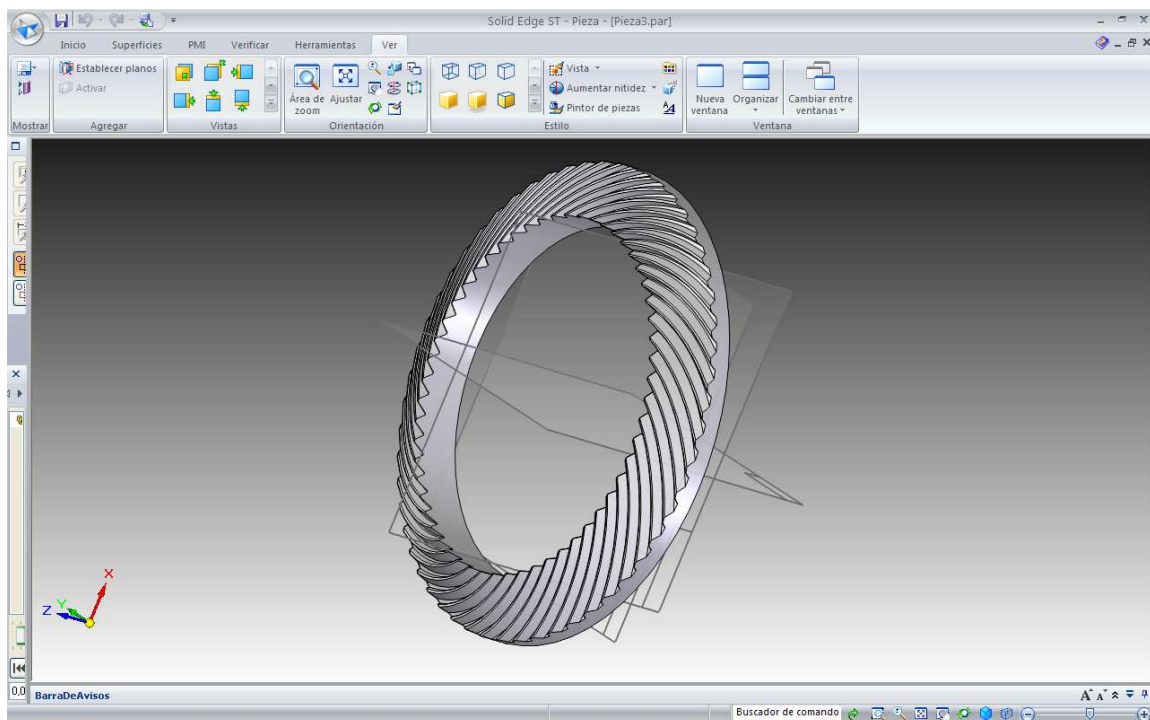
Diseño de engranaje hipoide en Solid Edge.
